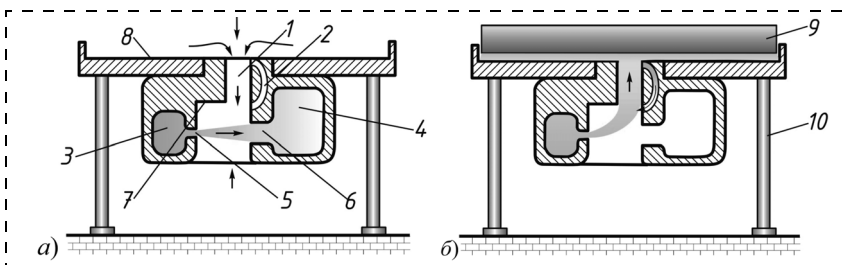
Сечение несущей поверхности пневмоконвейера и питающего сопла:
